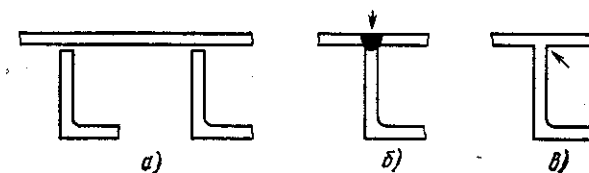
Соединение обшивки панелей со стрингерами способами сквозного проплава и диффузионной сварки:
